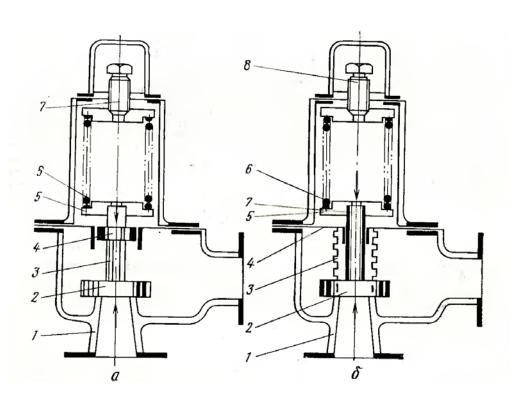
Уравновешенный пружинный предохранительный клапан а - балансировка при помощи поршня: 1- сопло, 2 - золотник, 3 -шток, 4 -поршень, 5 - шайба опорная, 6 -пружина, 7 - винт регулировочный;
